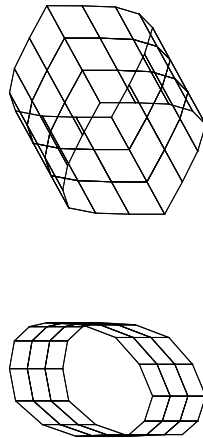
Конструктивна схема гранної бокової поверхні робочої камери.
